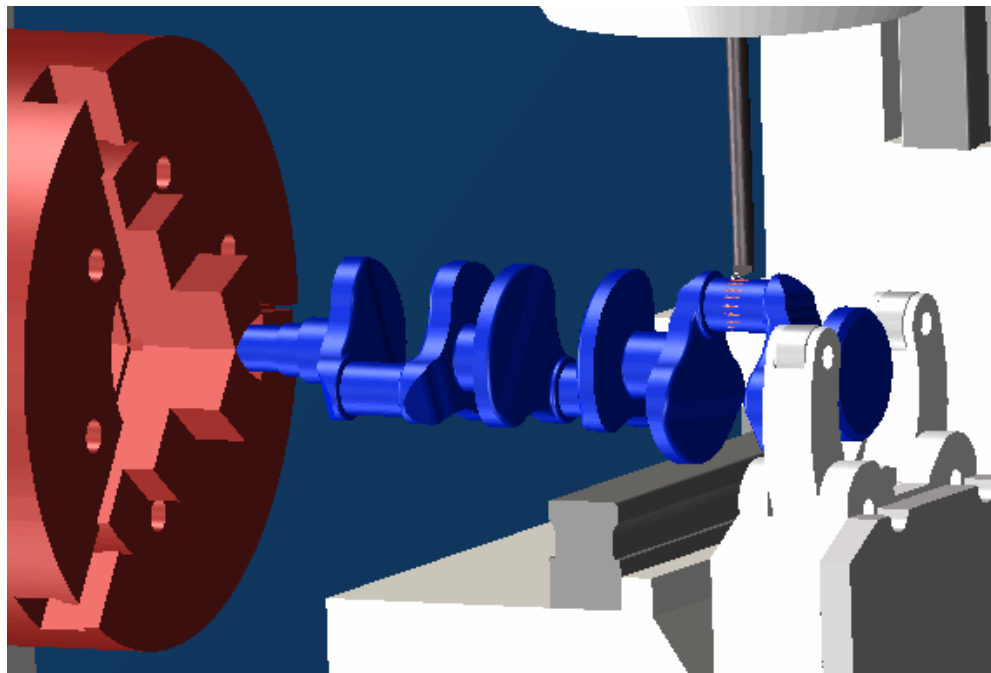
Виконання процесу фрезерування ексцентрикової поверхні [15]
